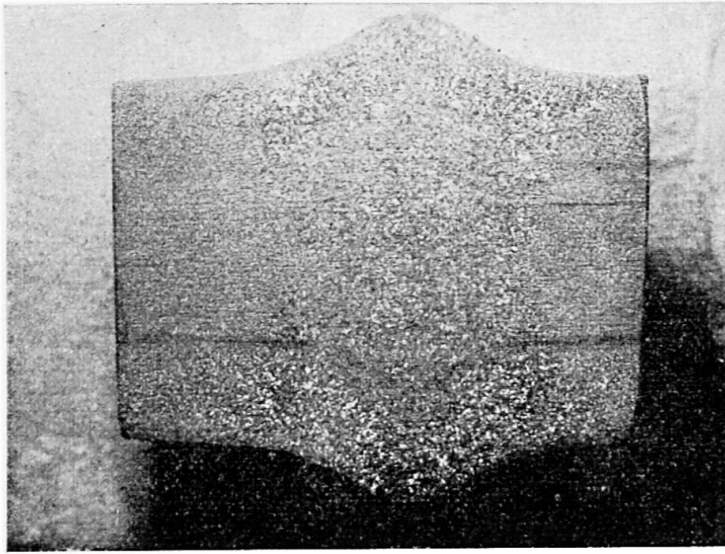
Coupe longitudinale et macrographie d'un joint soudé par résistance.
